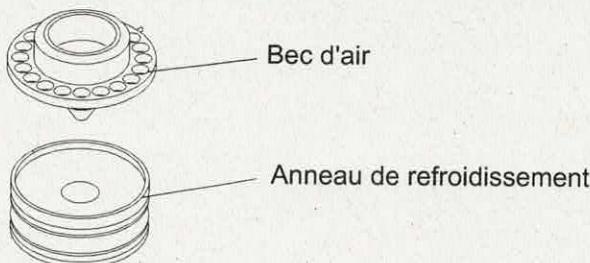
Buse d'air et bague de refroidissement (pièces dépendants de format)
